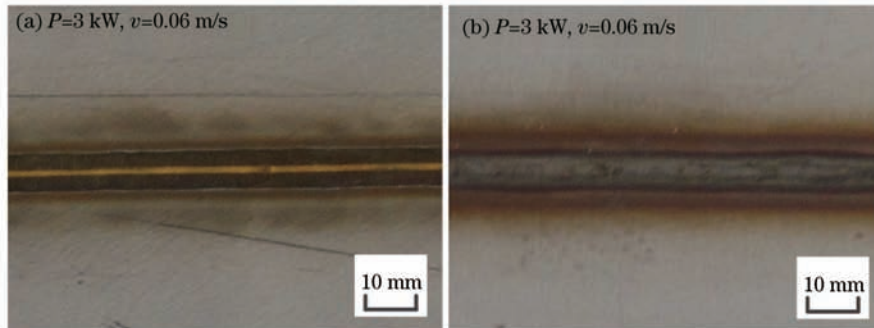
焊缝表面形貌图。(a)经氩气保护的焊缝形貌;(b)无保护的焊缝形貌
